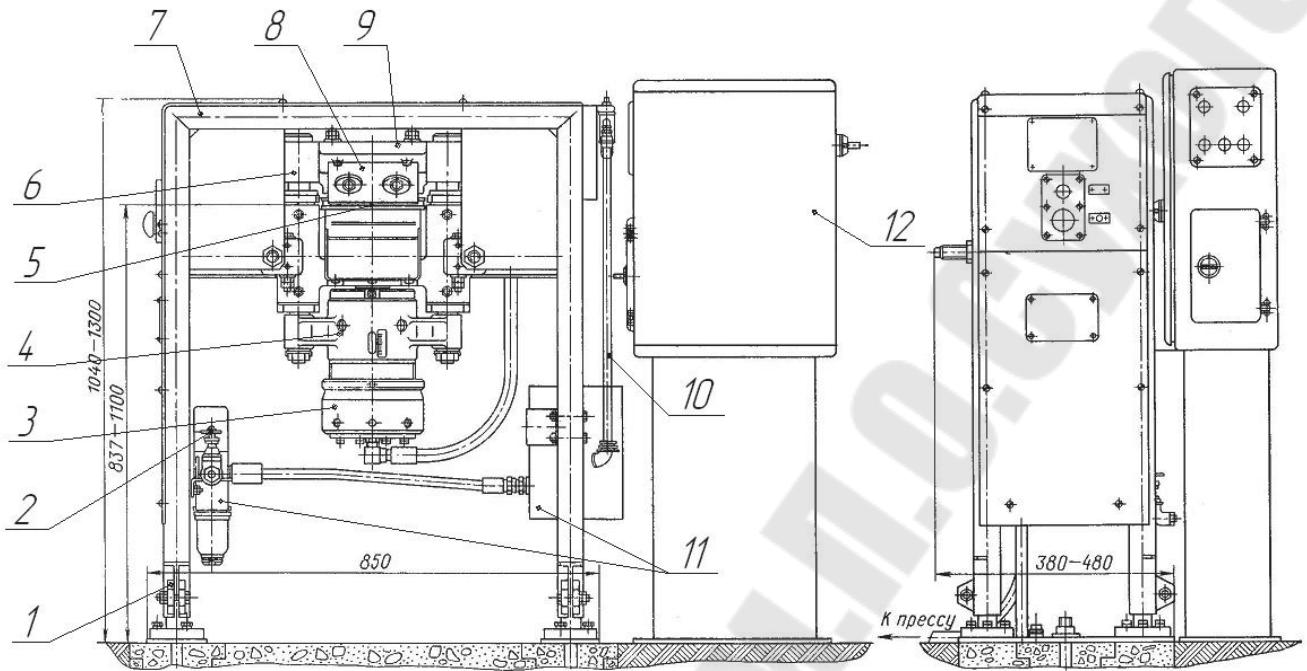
Общий вид модели НП1: 1 - клемный зажим; 2 - запорный вентиль; 3 – пневмоцилиндр; 4 - силовой блок; 5 - нижний нож; 6 – колонна; 7 – рама; 8 - верхний нож; 9 – траверса; 10 – воздухопровод; 11 - узел подготовки воздуха; 12 - электрооборудование
